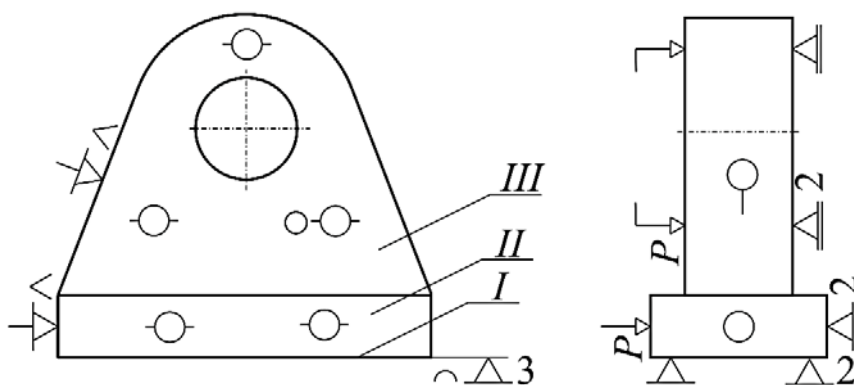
Принципиальная схема приспособления для сборки проушины
